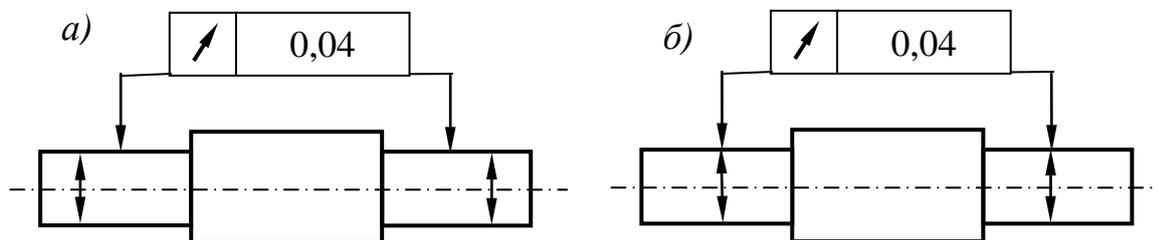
Размещение рамки допуска формы или расположения:
